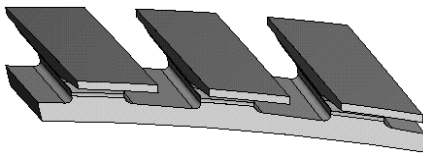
Зразок для випробувань на втому з ободної частини диска КВД дв. Д-36
